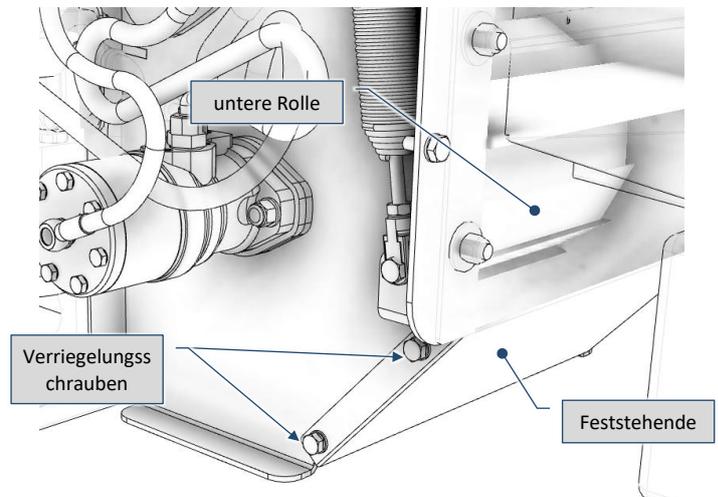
Detail des Einfülltrichters (Hydraulikzuführrollen)
